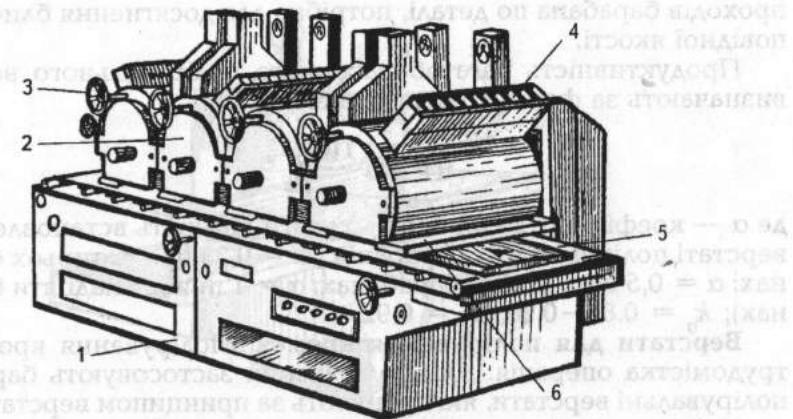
Чотирибарабанний полірувальний верстат П4Б:
